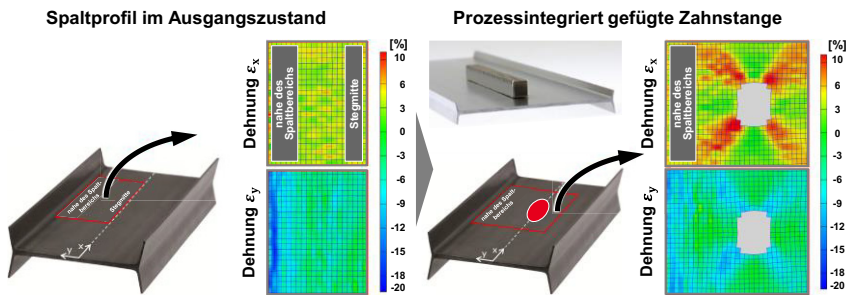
Prozessintegriert mechanisch gefügte Zahnstange⁷⁹
